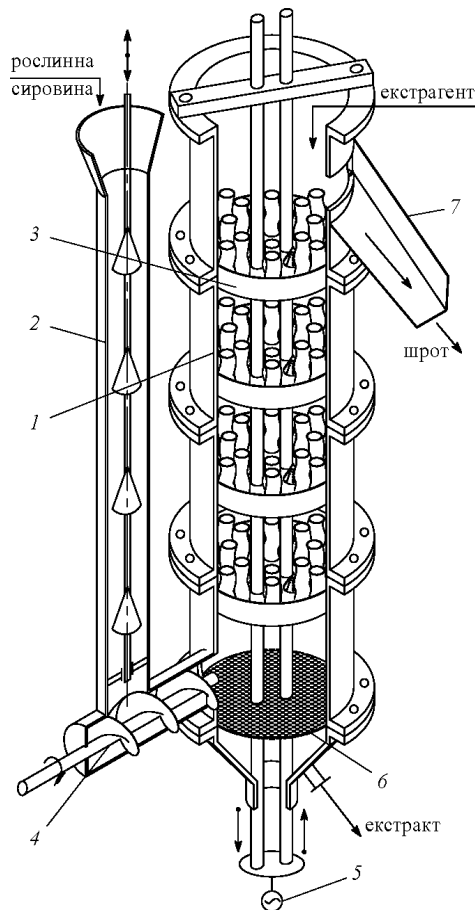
Загальний вигляд лабораторного віброекстрактора безперервної дії: 1 – корпус; 2 – завантажувальний пристрій; 3 – тарілки; 4 – шнек; 5 – вібропривід; 6 – фільтрувальна решітка; 7 – лоток.
